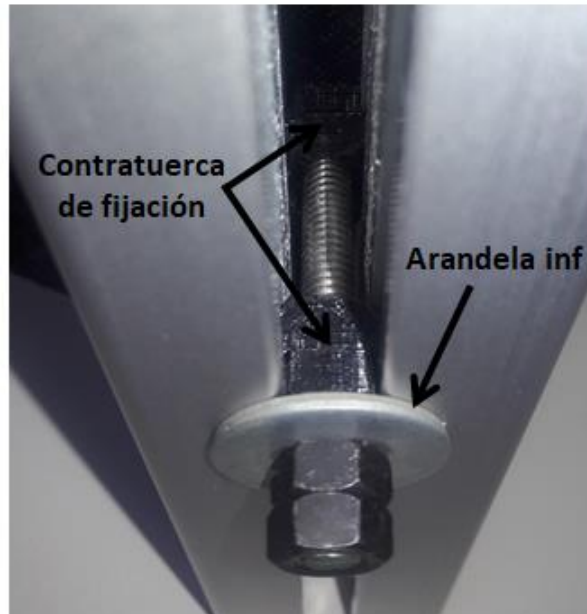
Vista inferior del ensamblaje sobre el voladizo
